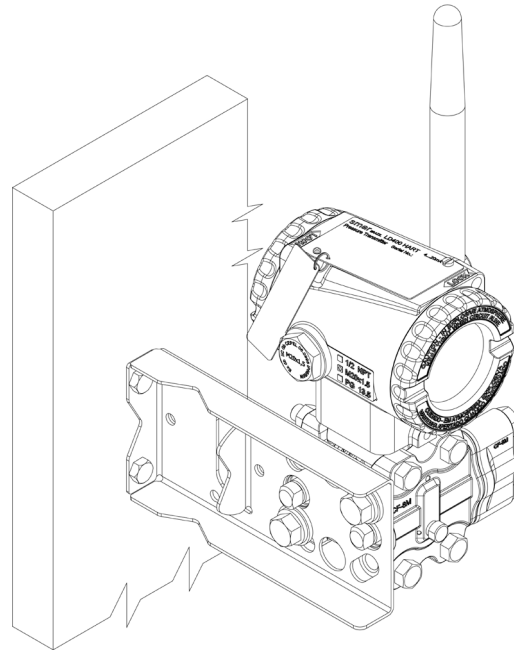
(g) – Desenho Dimensional de Montagem do LD400 WirelessHART™ - Transmissor de Pressão com Haste de Inserção
